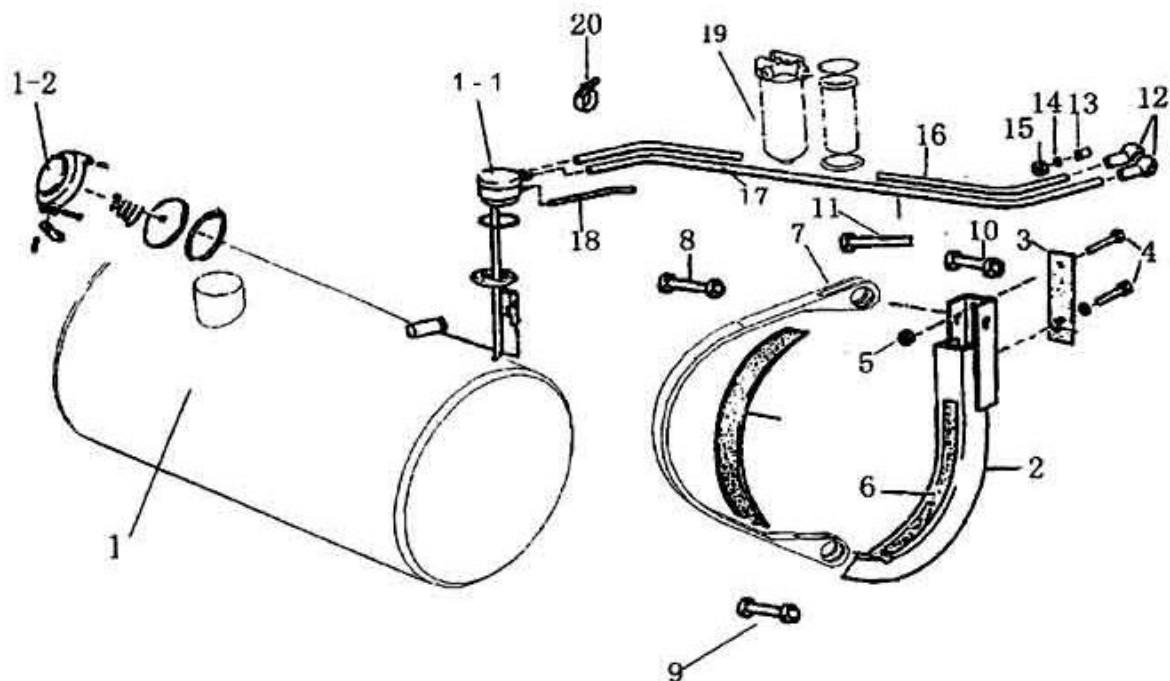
Алюминиевый топливный бак в сборе.
